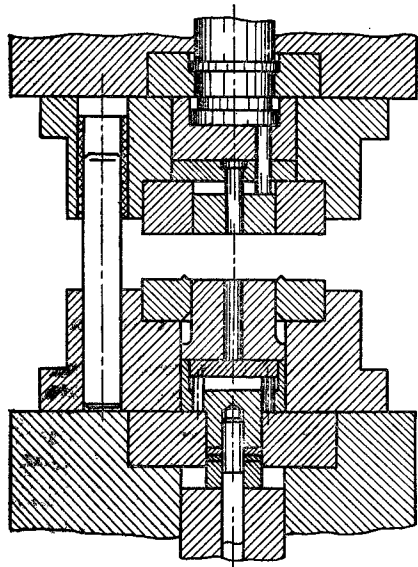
Штамп для чистой вырубки для прессы тройного действия (с подвижным пуансоном)
